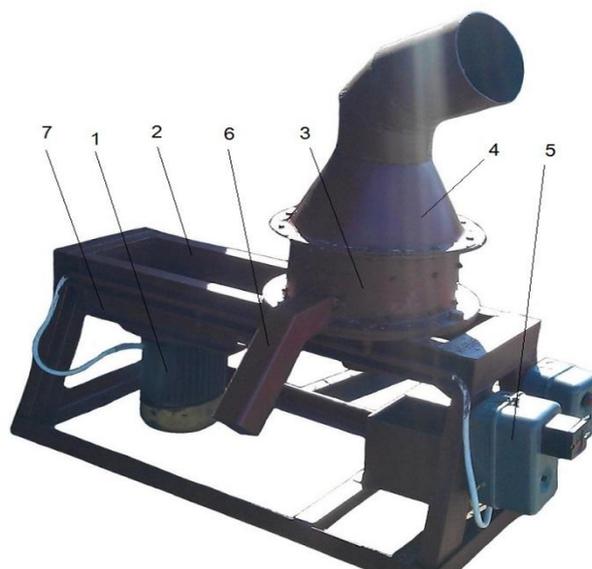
Роторная мельница: 1 – фланцевый электродвигатель; 2 – станина; 3 – корпус дробилки; 4 – загрузочный бункер; 5 – пусковое устройство электродвигателя; 6 – выгрузной желоб; 7 – натяжное устройство
